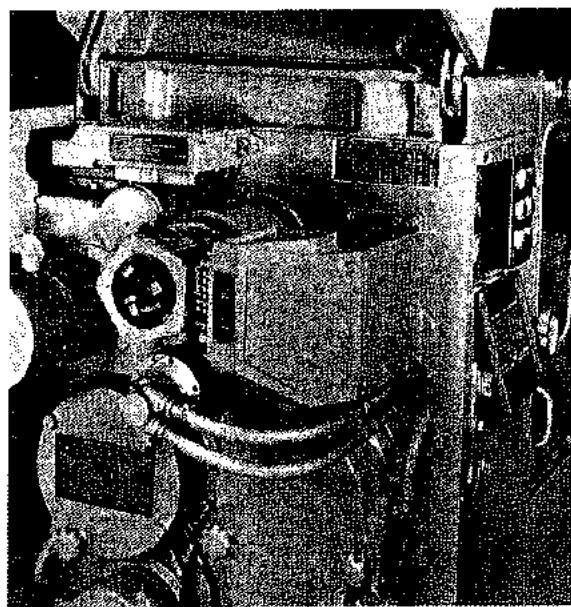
Terminal de mando de una máquina de mandril automático y de un solo husillo (Warner & Swasey Co.)
